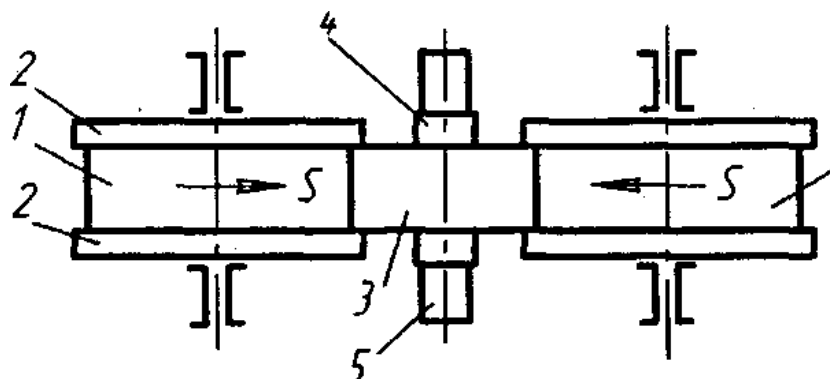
Схема горячего накатывания зубьев: 1 – накатники; 2 – реборды; 3 – заготовка; 4 – переходная втулка; 5 – оправка
